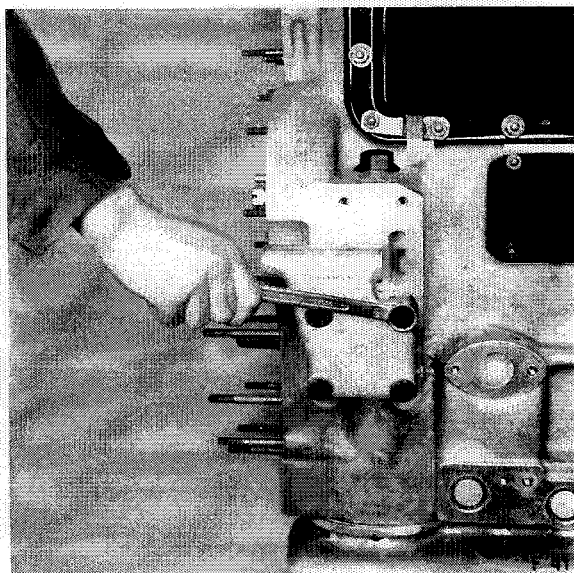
Lösen der Befestigungsschrauben am untern Support für den Dynamo
